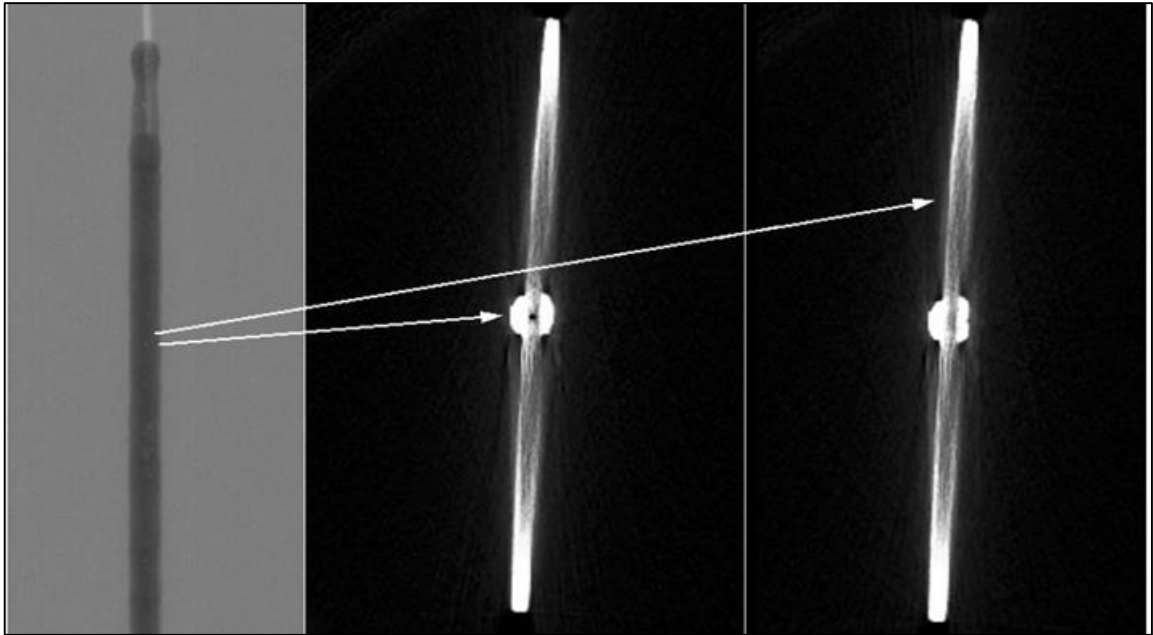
Imagen radiográfica de soldadura frontal, cortes de las secciones señaladas donde se pueden observar poros.
